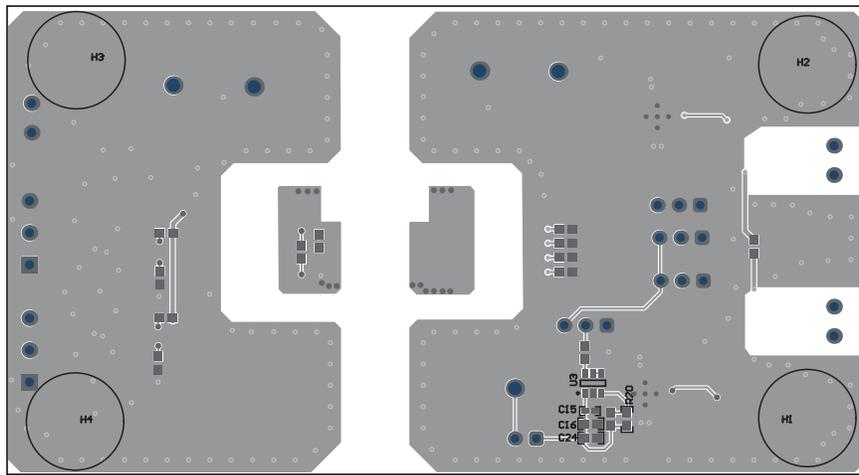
ISOW3080DWEEVM PCB 布局 - 底层
